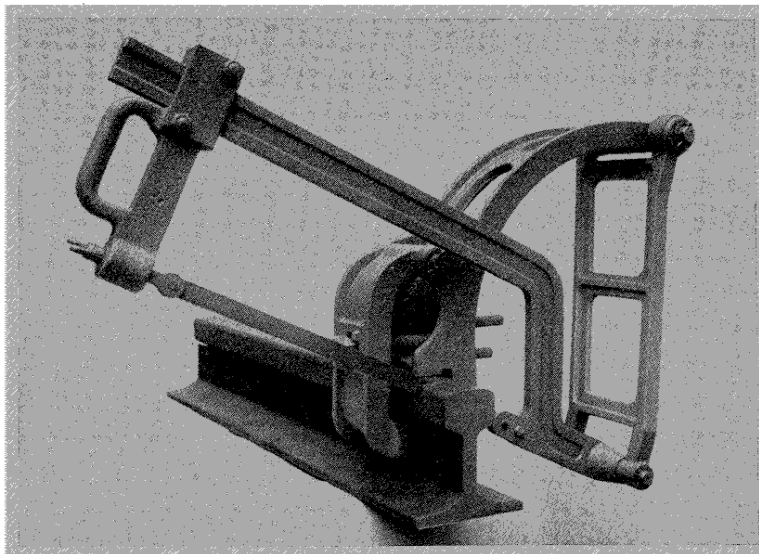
Machine portable à scier les rails de chemins de fer.
